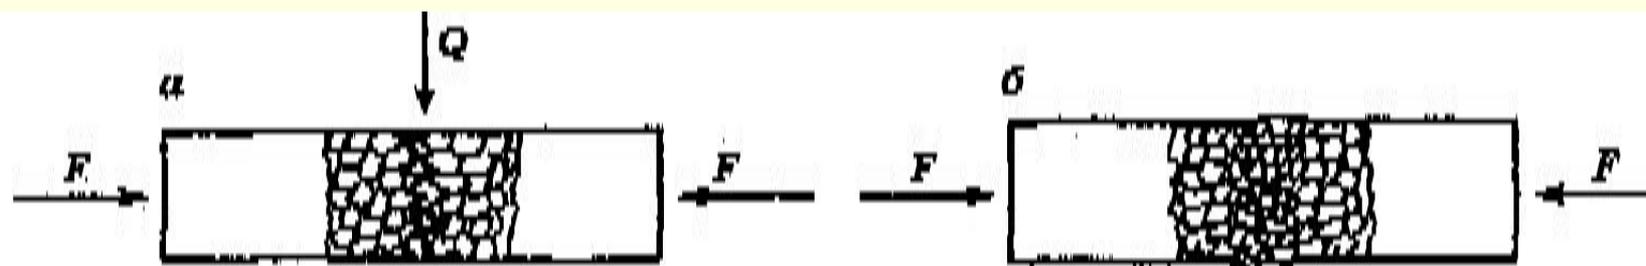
Схема образования сварного соединения при сварке давлением:
